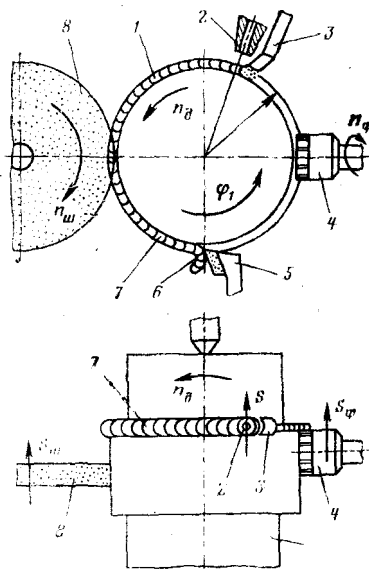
Схема совмещенной комплексно-механизированной технологии одновременной наплавки, удаления шлаковой корки, фрезерования и шлифования наплавленного металла: 1 — деталь, восстанавливаемая наплавкой; 2 — мундштук сварочного аппарата для подачи наплавочной проволоки; 3 — устройство для подачи и удержания флюса; 4 — валик наплавленного металла; 5 — шлаковая корка; 6 — резец, удаляющий шлак; 7 — фреза; 8 — шлифовальный круг
